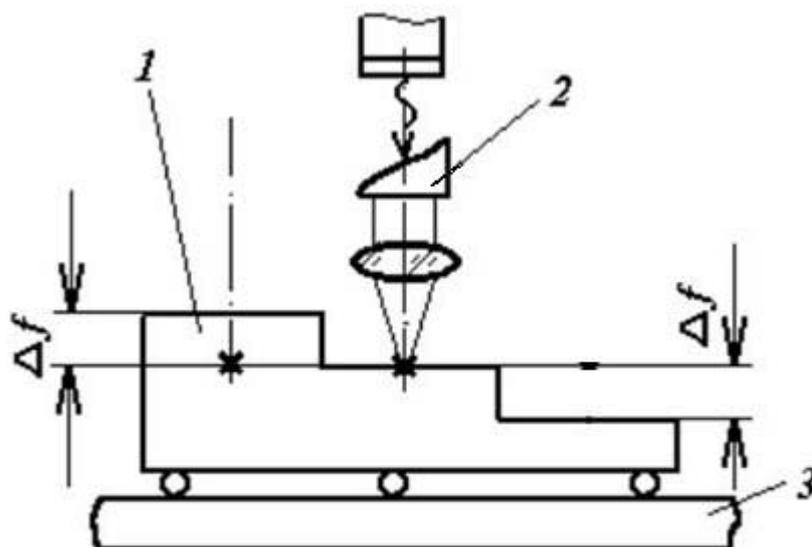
Схема настройки ЛТУ с помощью дополнительной оптики: 1 – заготовка; 2 – фокусирующая система; 3 – рабочий стол
